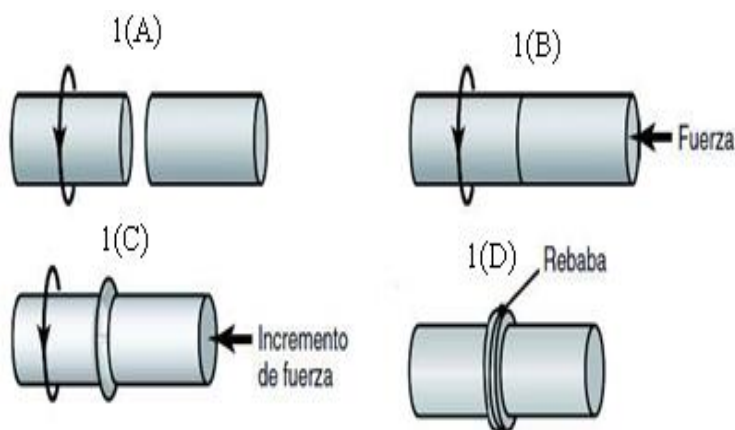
Principios de la soldadura por fricción. Fuente: Mishra (2014).
